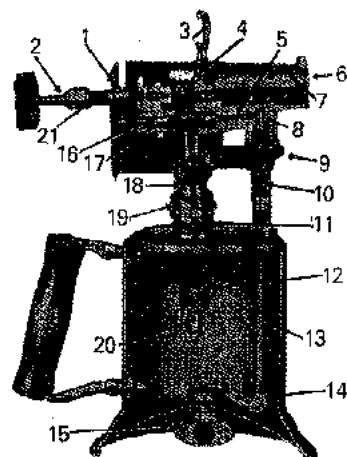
Vista en sección de una lámpara de soldador (Clayton & Lambert Mfg. Co.)
